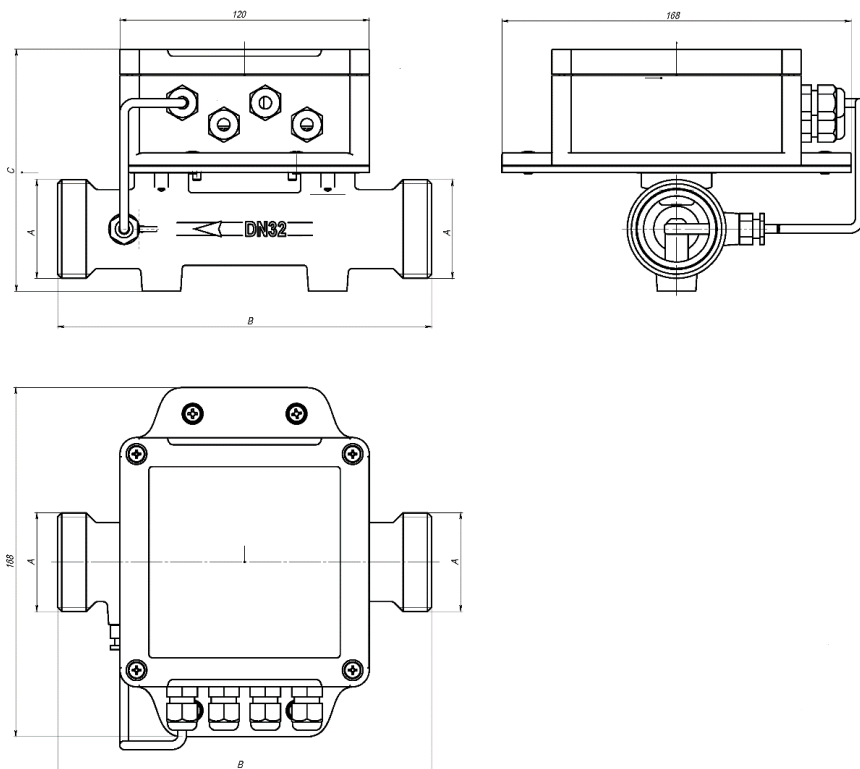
Габаритные и присоединительные размеры для расходомеров со степенью защиты оболочки IP68 совмещенного исполнения
